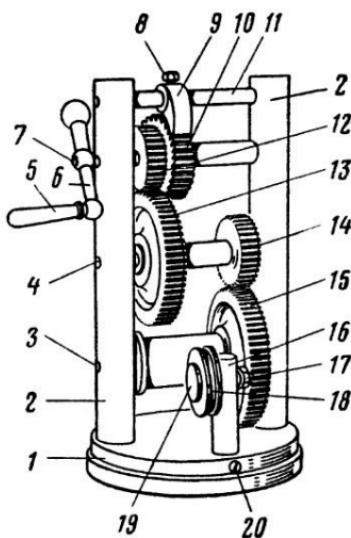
Модель лебедки (передача с цилиндрическими зубчатыми колесами): 1 — основание; 2 — стойка; 3 — ведомый вал; 4 — промежуточный вал; 5 — ручка; 6 — рычаг ручки; 7 — вал привода; 8 — стопорный винт; 9 — собачка; 10 — храповое колесо; 11 — ось; 12 — ведущее колесо; 13 — ведомое колесо; 14 — ведущее колесо; 15 — ведомое колесо; 16 — стойка; 17 — гайка; 18 — ролик; 19 — ось; 20 — стопорный винт.
